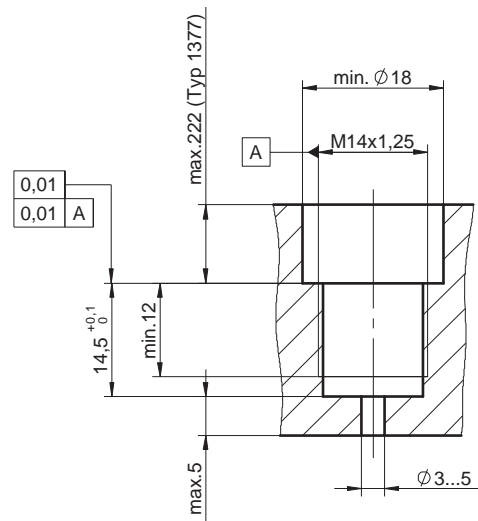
Zurückversetzt eingebauter Sensor. Bohrungsdurchmesser gemäss Montagewerkzeug.
